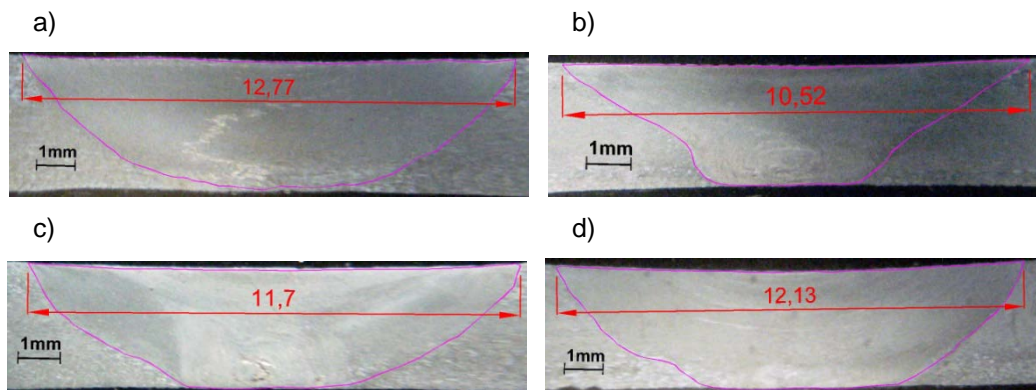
Macrográficas de probetas soldadas T con pin cuadrado: a) 1Cu-T; b) 2Cu-T; c) 3Cu-T y d) 4Cu-T.
